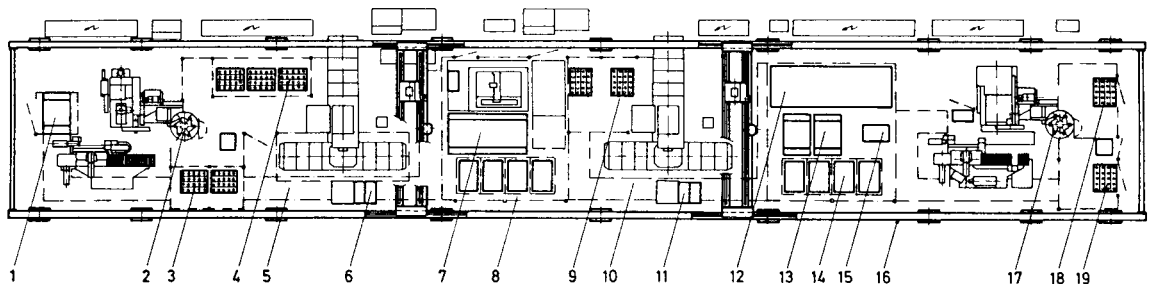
Flexibles Fertigungssystem für Werkstücke mit unregelmässigen Formen
